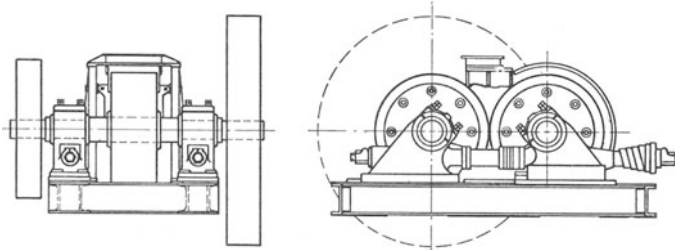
Walzwerk zur Erzeugung von Quetschsand.
